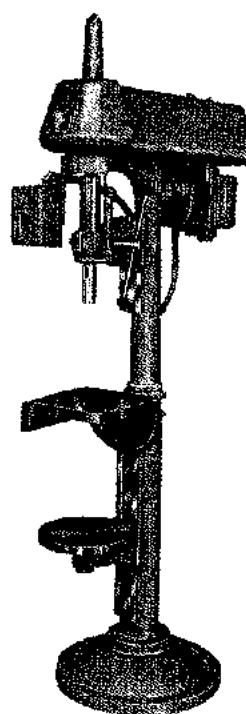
Taladradora sensible (Cincinnati Lathe & Tool Co.)
